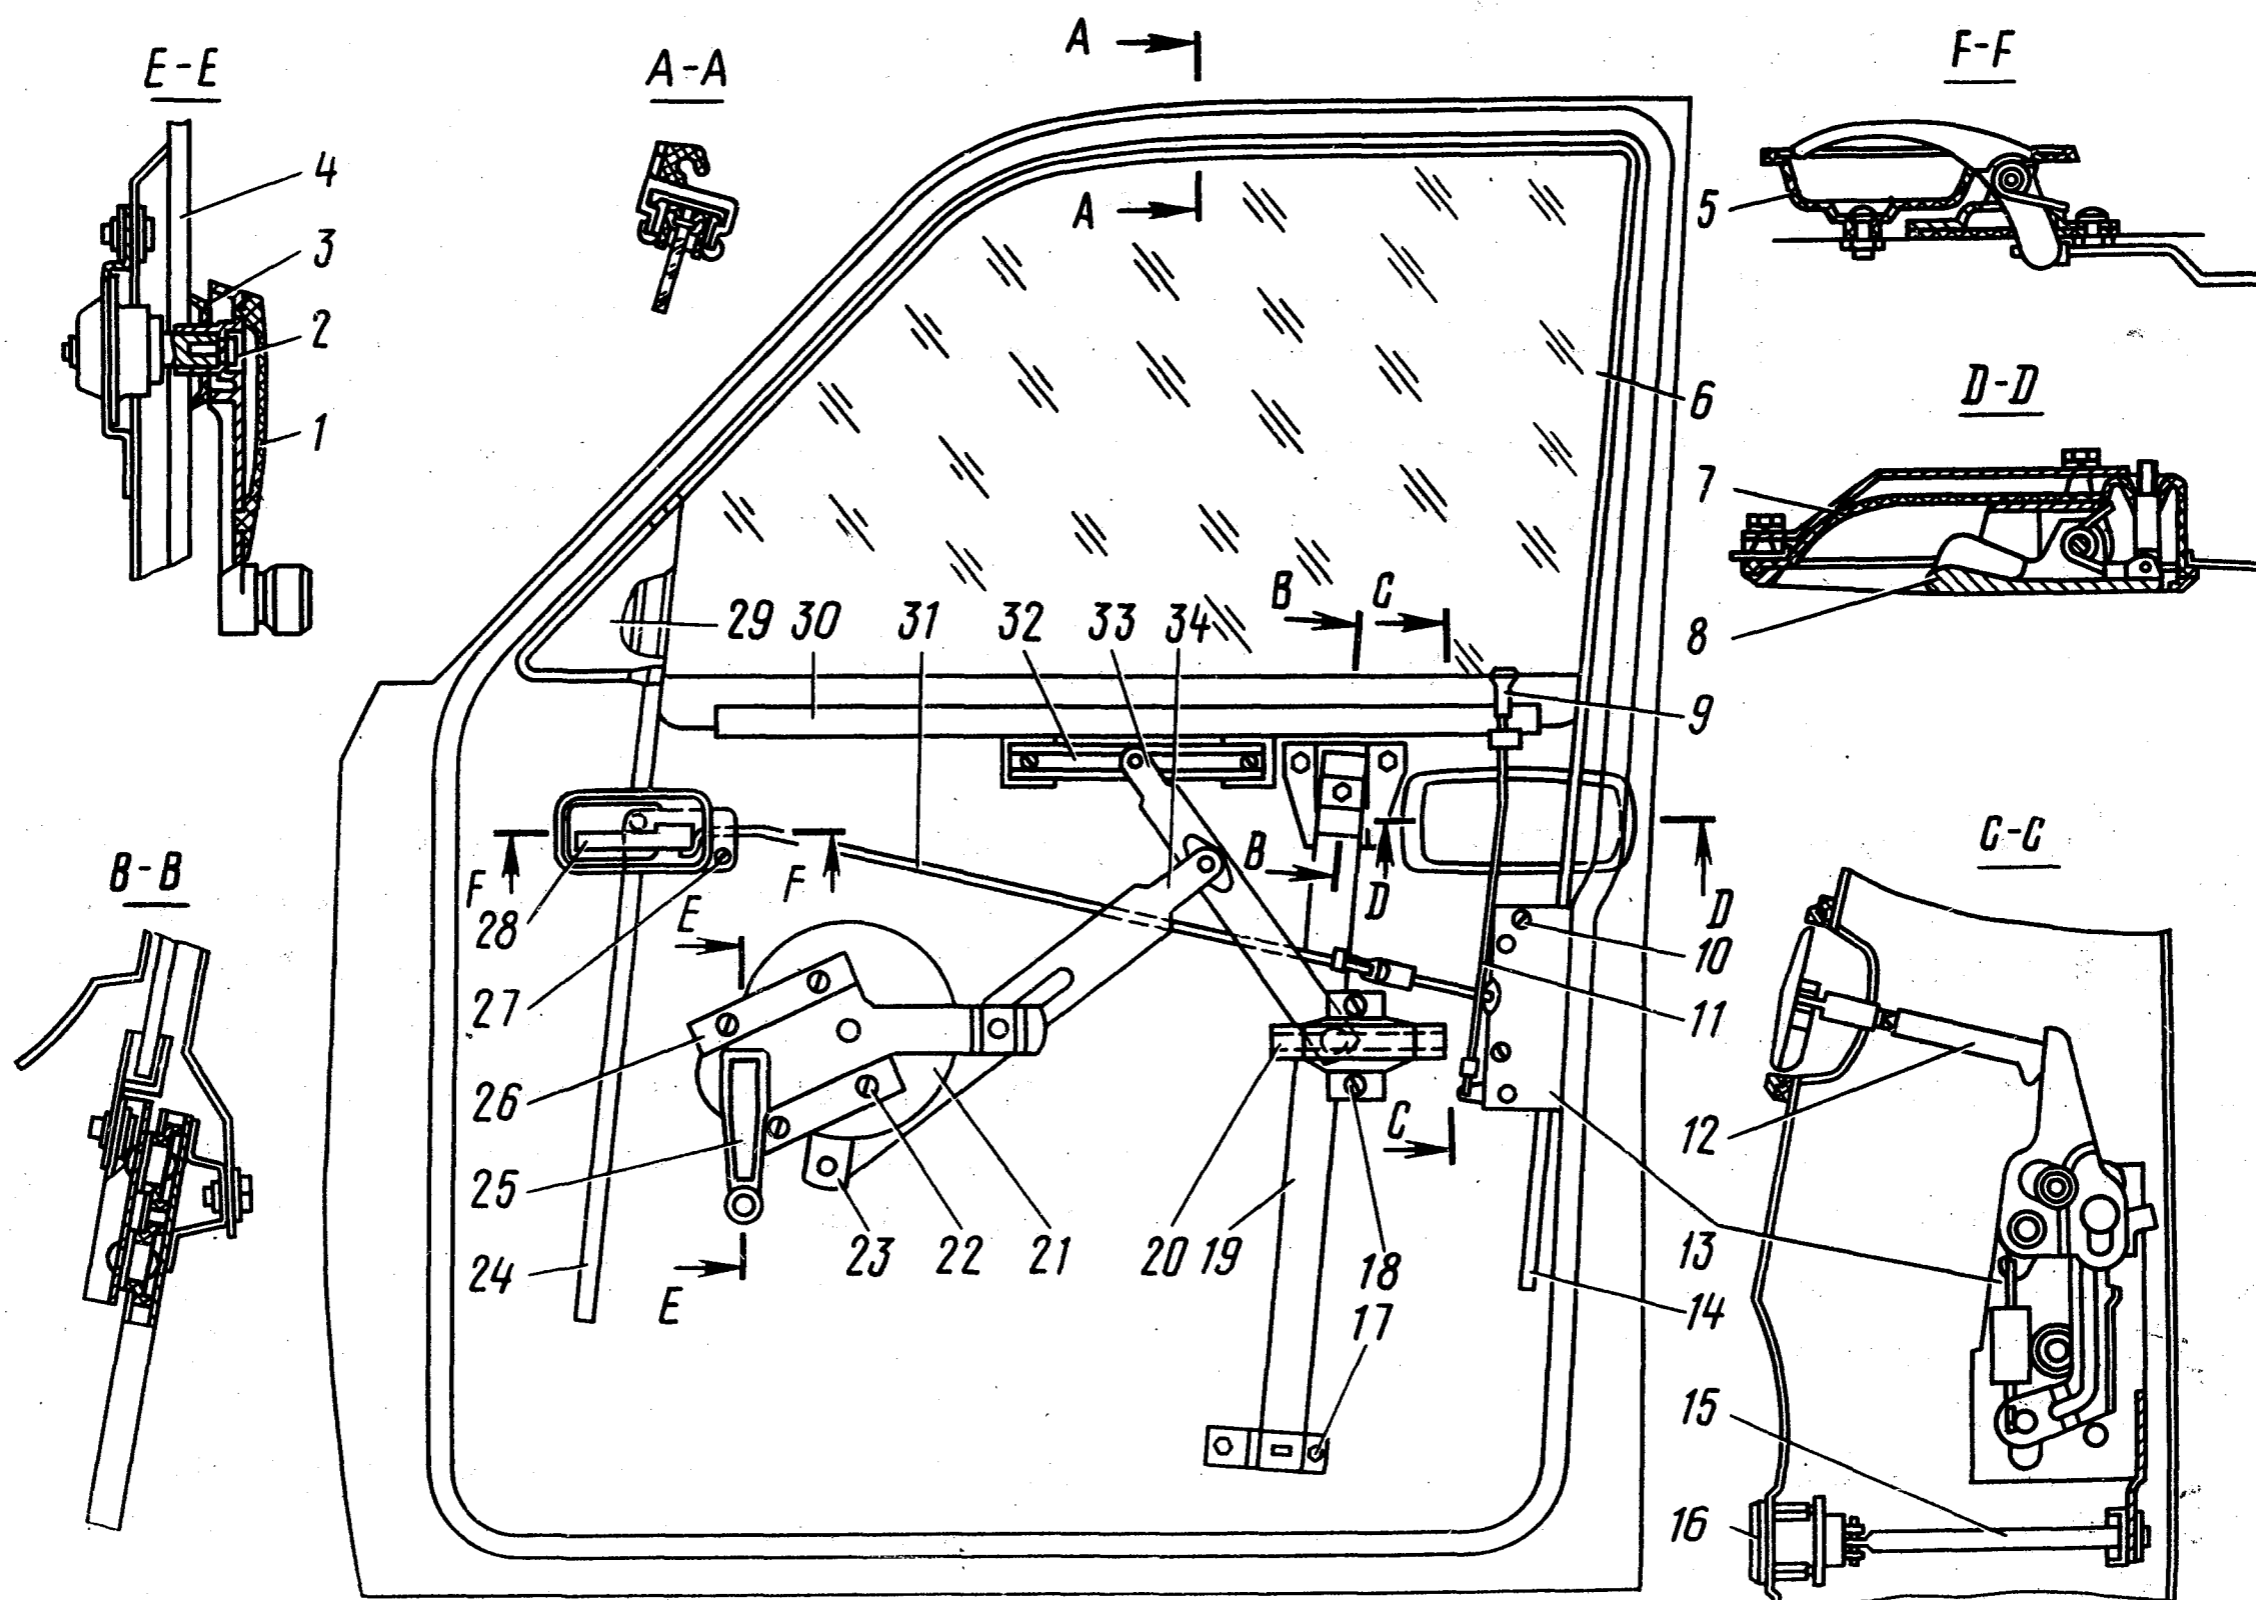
Стеклоподъемник, замки дверей и их установка:
